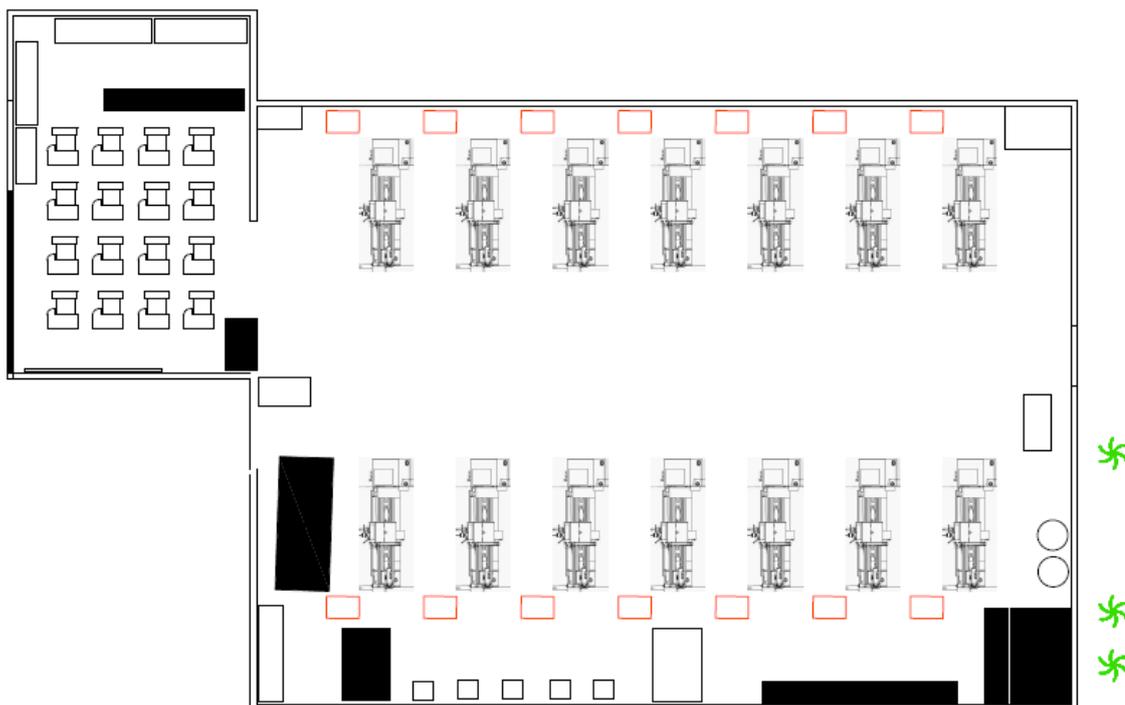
Croquis de la distribución actual del Taller 04 Torneado Mecánico
